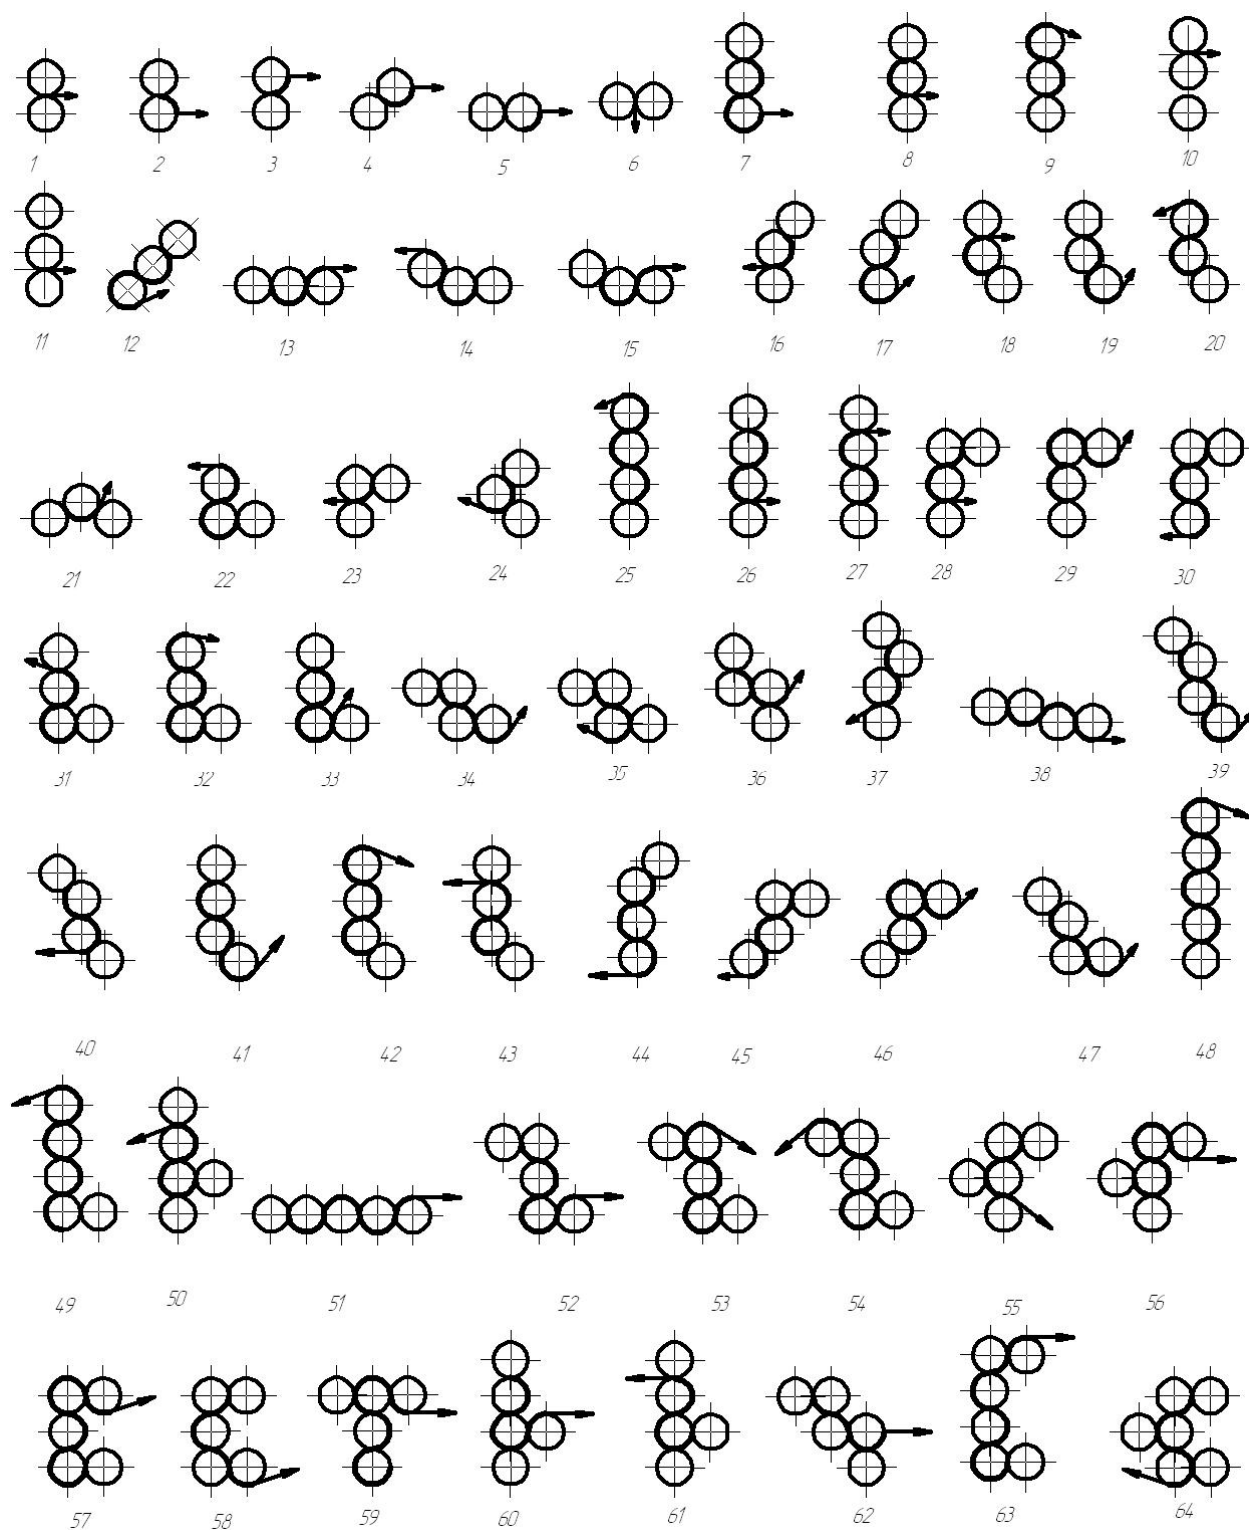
Схеми руху формованого виробу по валках каландра під час листування
